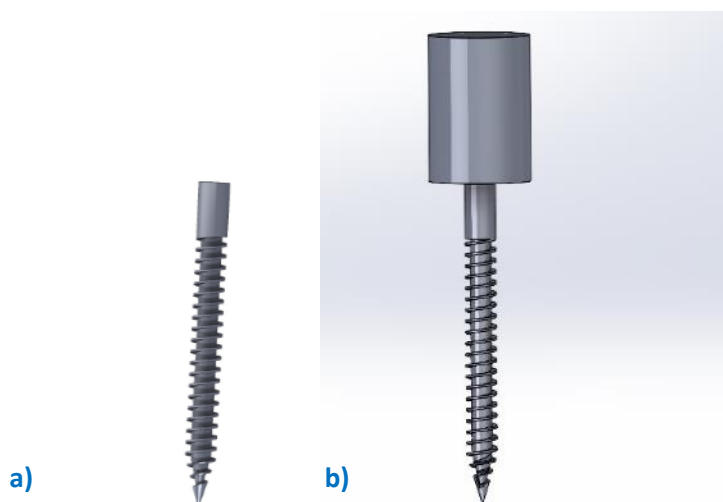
Disegno della vite: a) vista 3D; b) vite con sistema di montaggio
